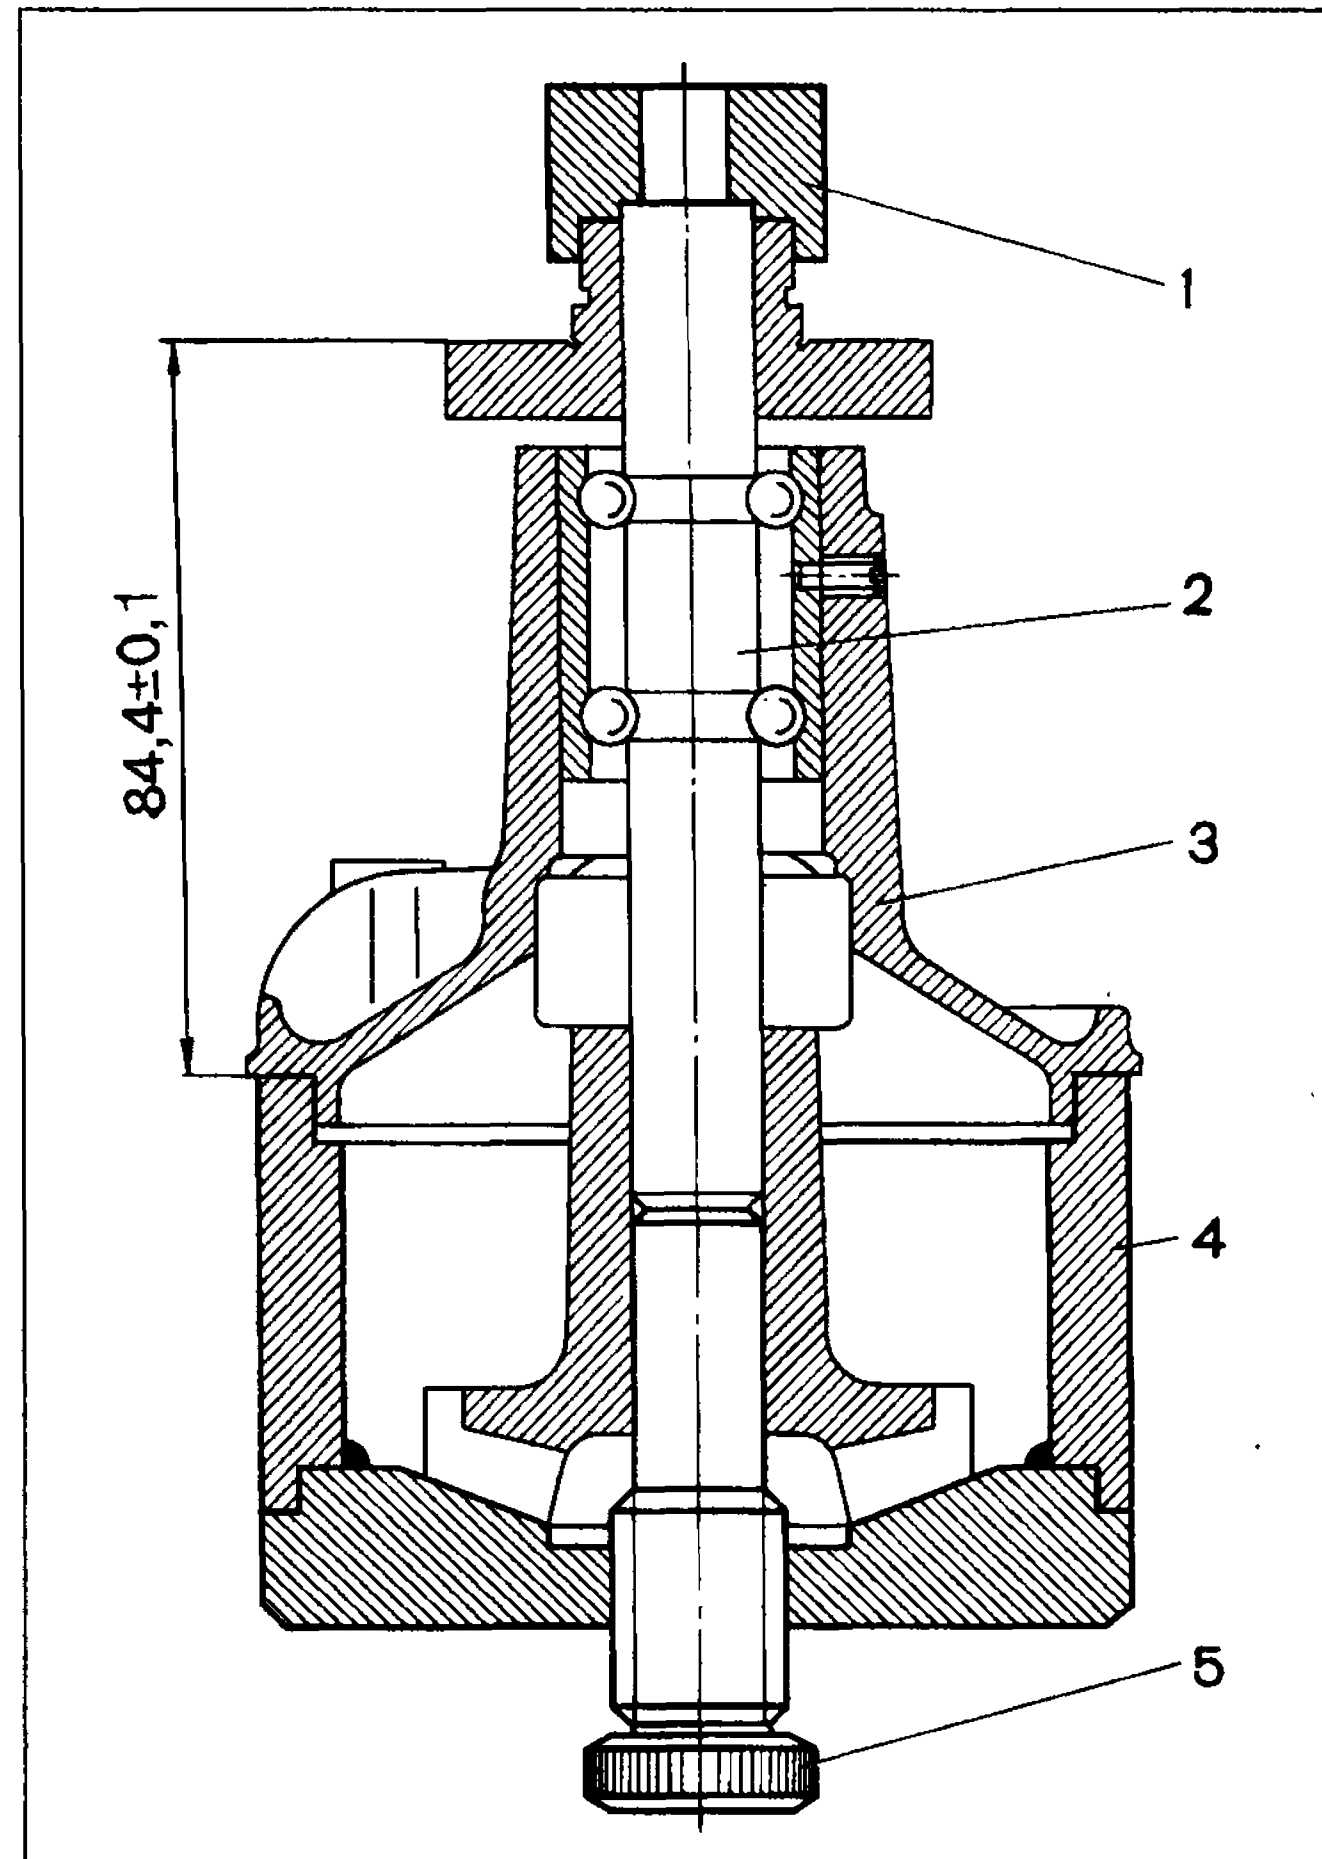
Напрессовка крыльчатки на вал насоса приспособлением А.60430:
